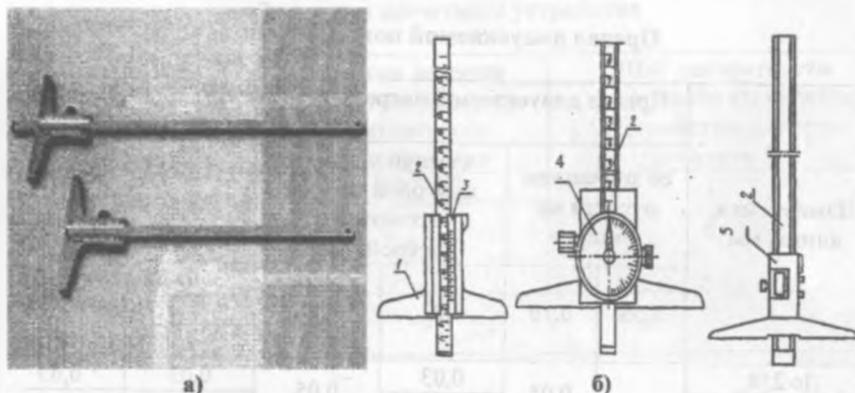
Штангенглубиномер: а) - общий вид, б) - устройство:
